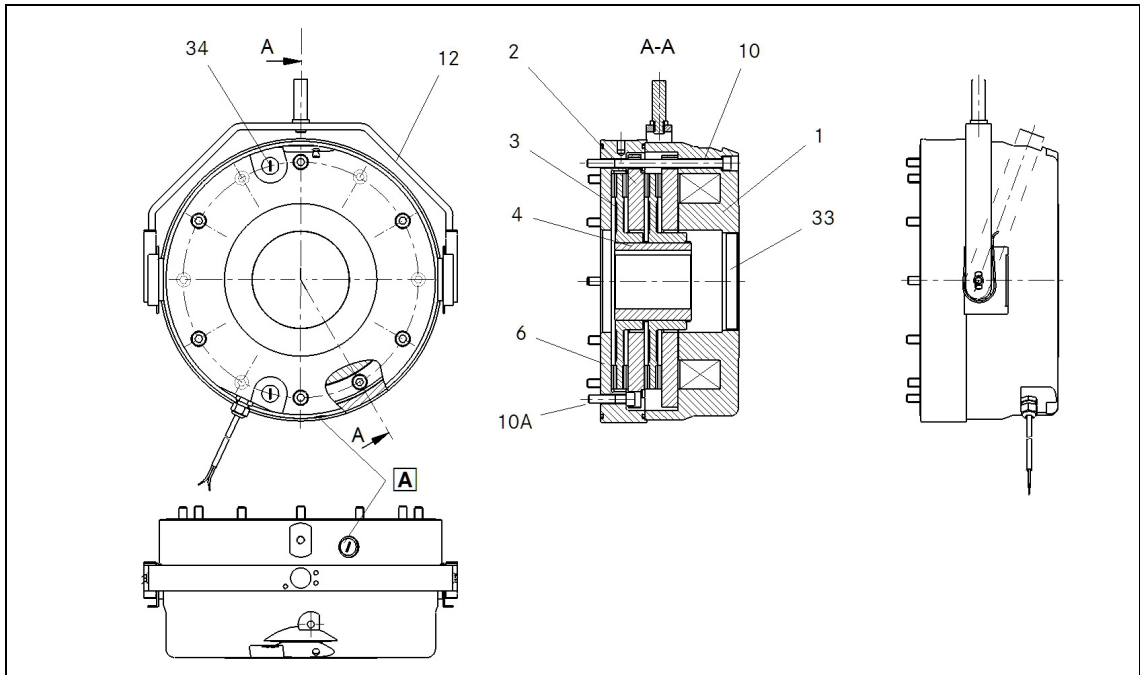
Aufbau der Federkraftbremse BFK471-25, Doppel-Rotor-Ausführung
